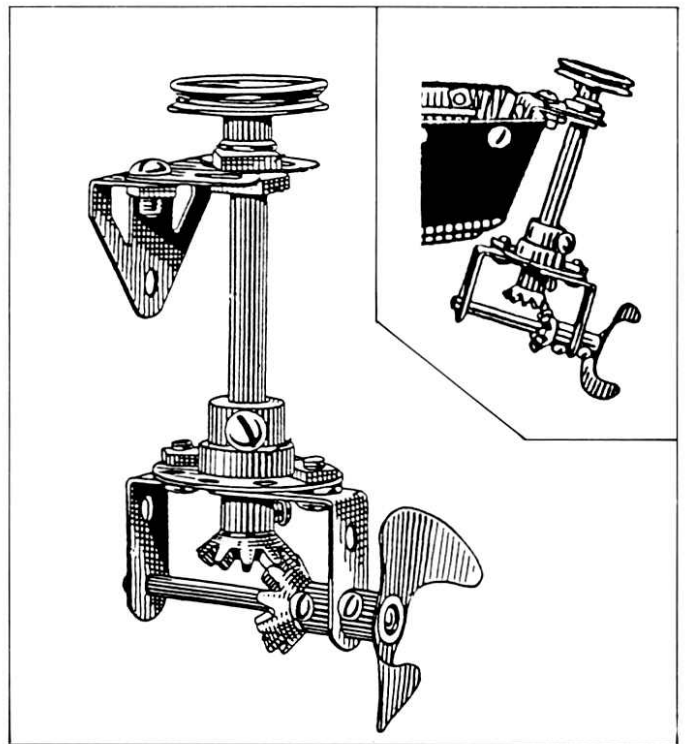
Construction du moteur hors-bord et détails d'installation.
